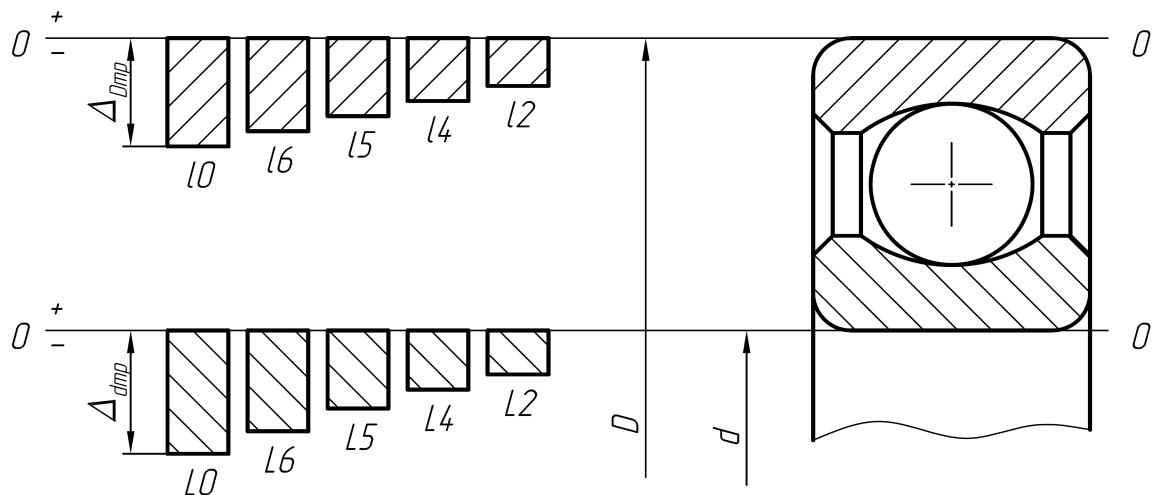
Схеми розташування полів допусків підшипників за класами точності
